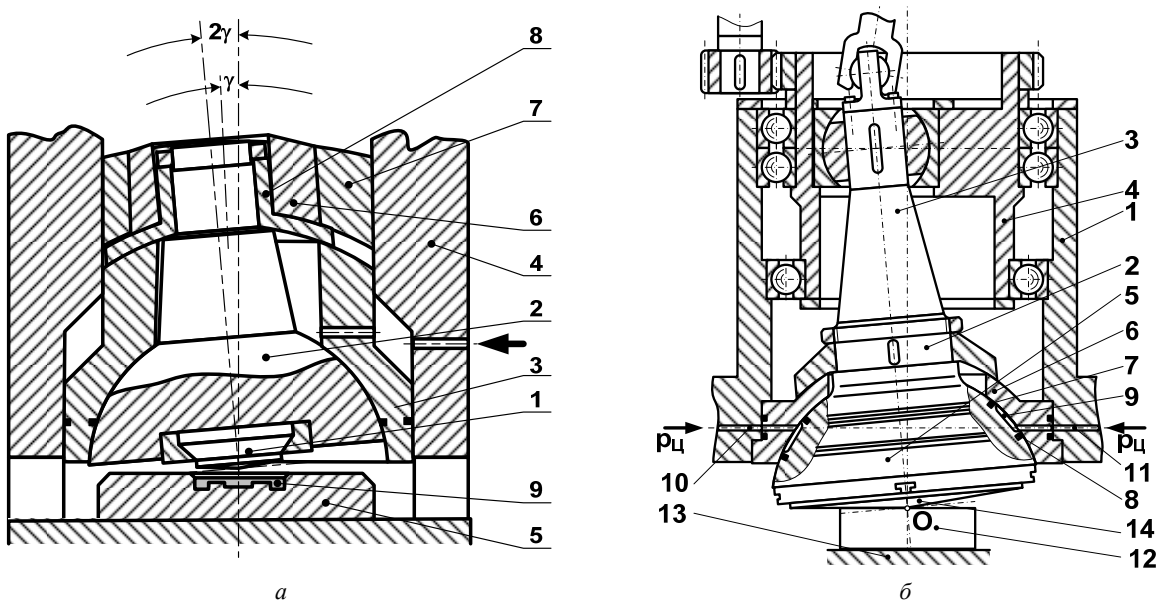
Схеми механізмів орбітального руху інструменту конструкції З. Марціняка (а) та конструкції з розміщення порожнини гідростатичного підшипника безпосередньо в сферичній частині пресувача (б)
